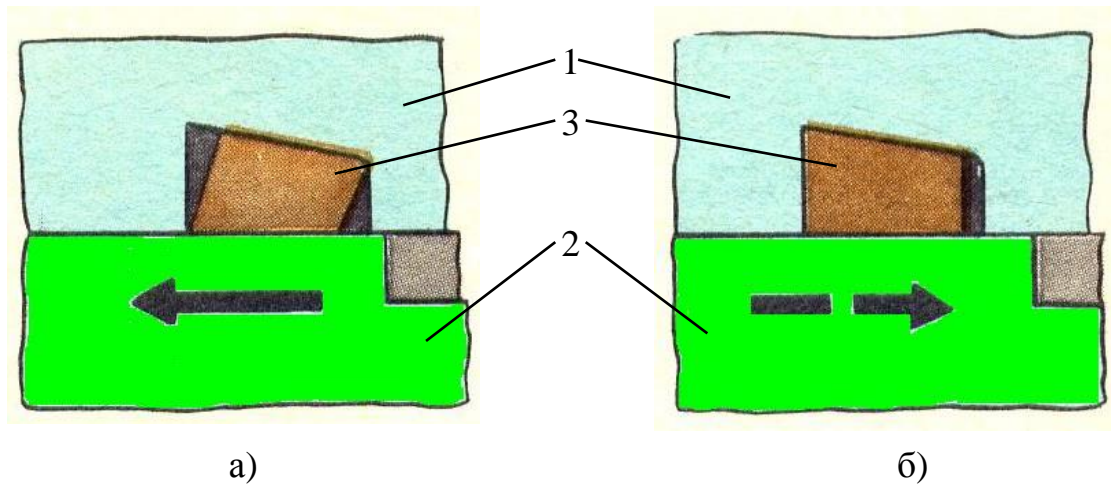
Схема работы уплотнительного кольца при торможении (а) и растормаживании (б) дискового тормозного механизма с гидравлическим приводом: 1 – рабочий цилиндр; 2 – поршень; 3 – уплотнительное кольцо
